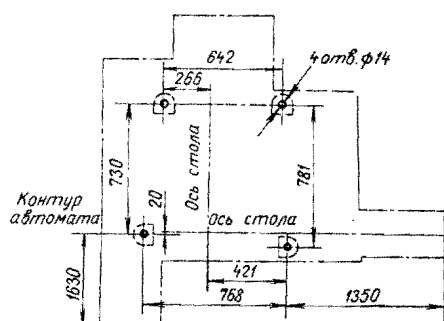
План расположения отверстий под фундаментные болты автомата марки АРМ
